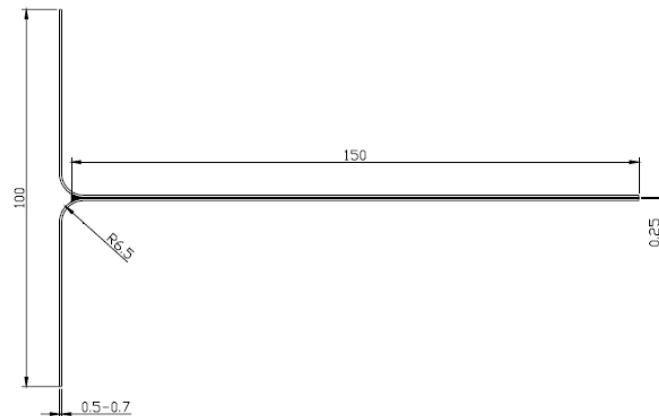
Geometria e dimensões (em mm) do ensaio de arrancamento T-peel [31].
